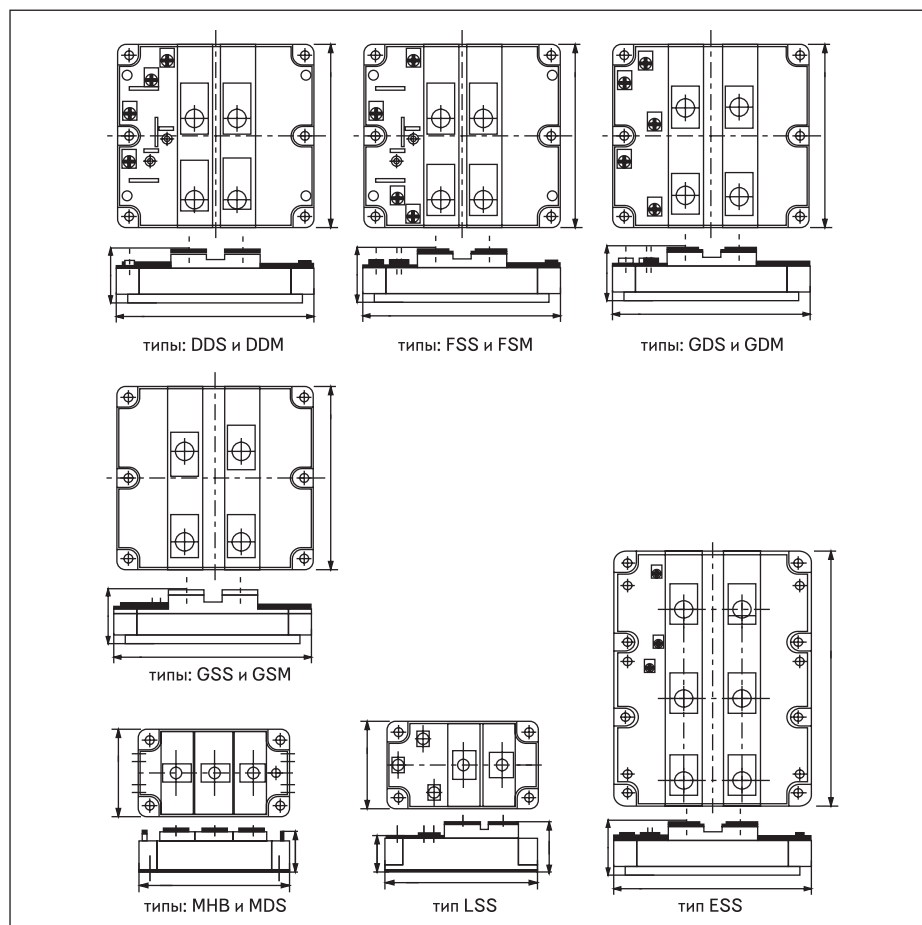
Профили и размеры различных типов корпусов IGBT модулей Duplex
